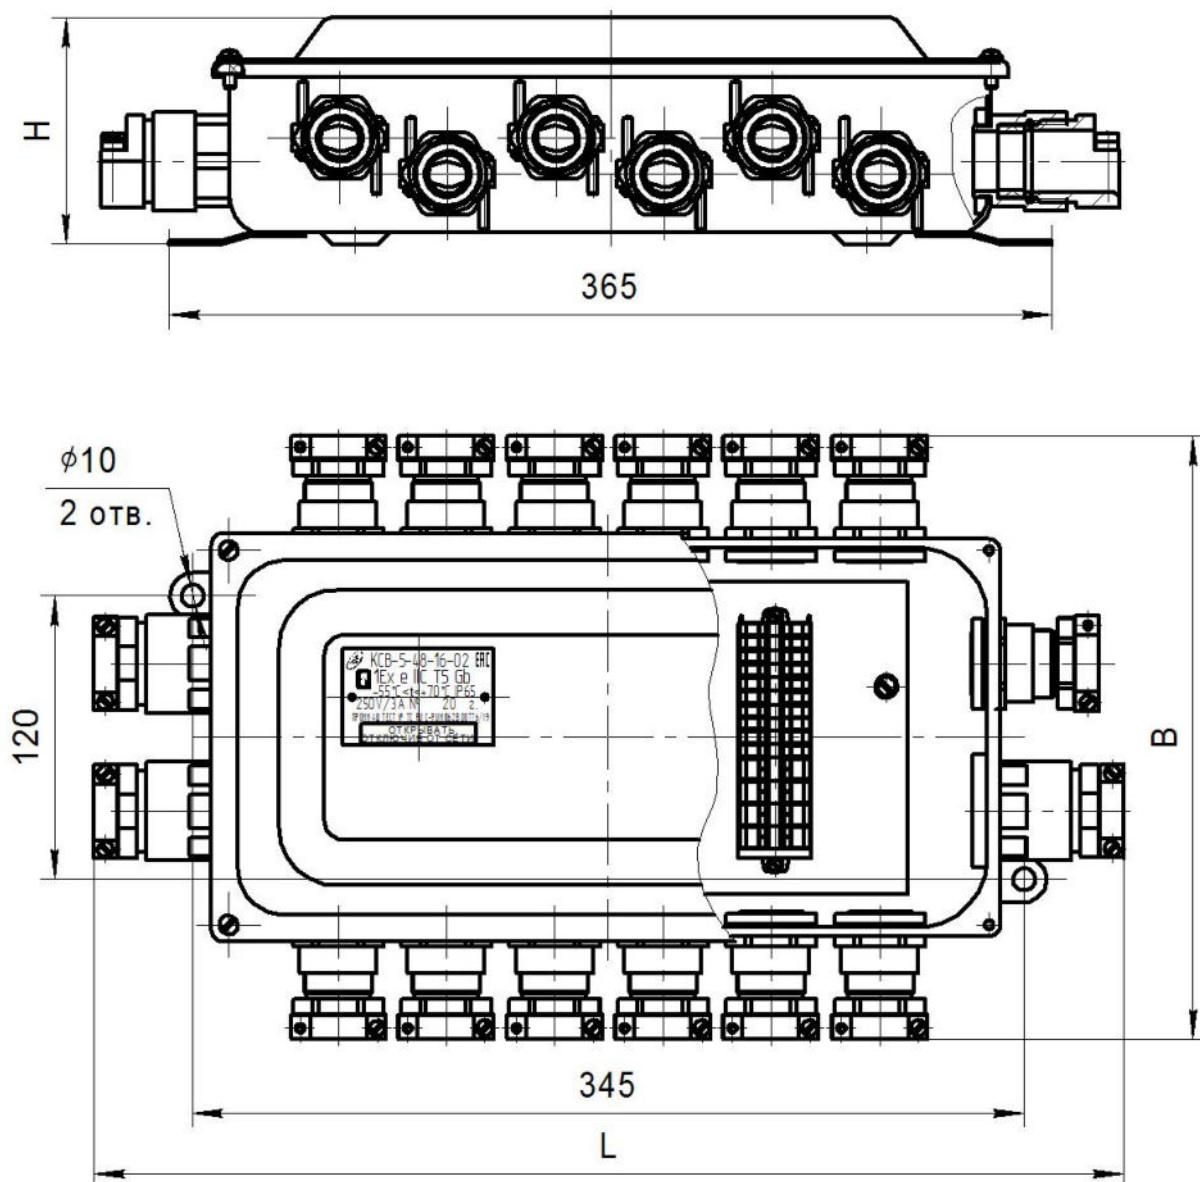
Габаритные и присоединительные размеры коробок:
